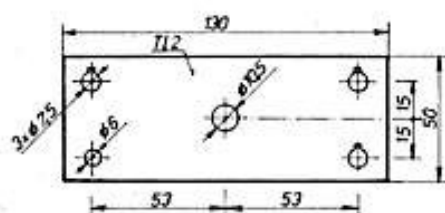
Zadní panel - Al polotvrdý - 1 ks
